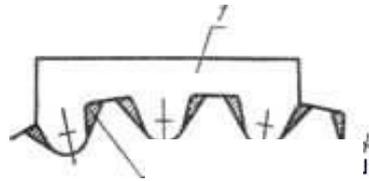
Наплавка зубьев звездочки: 1 — медный шаблон;
